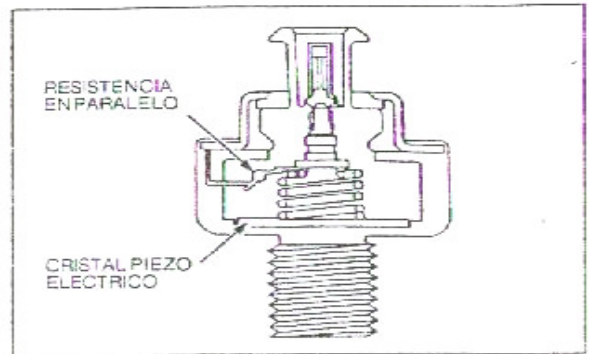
Sensor de Detonación Corte Longitudinal
